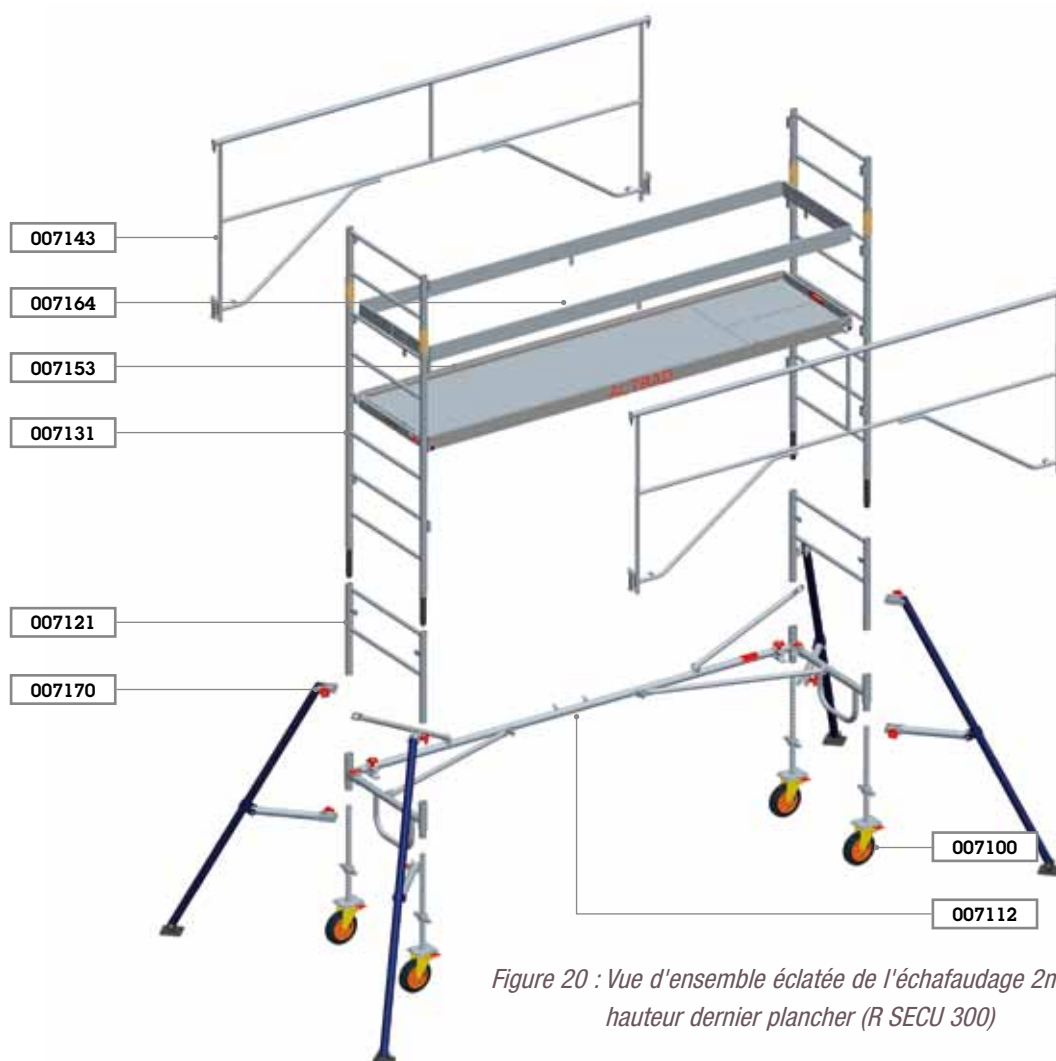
Vue d'ensemble éclatée de l'échafaudage 2m hauteur dernier plancher (R SECU 300)
